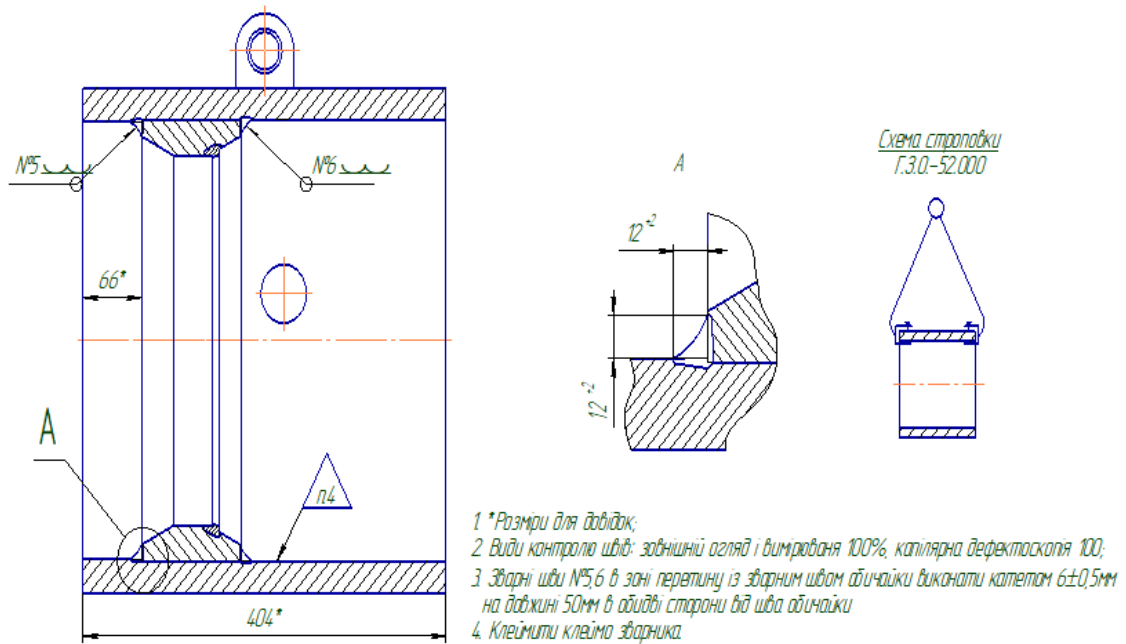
Ескіз приварювання кільця до корпусу
